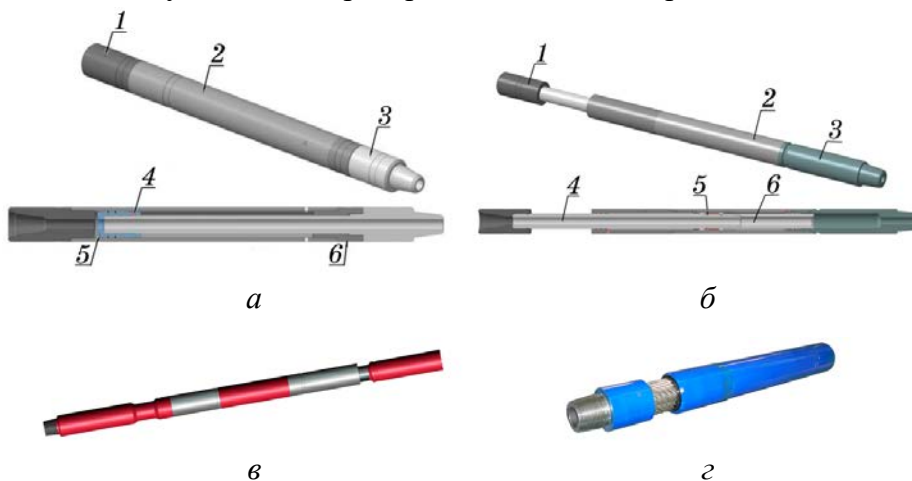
Яс: *а* – механічний (1 – корпус верхній, 2 – корпус, 3 – шток, 4 – шпеник, 5 – хвостовик штока, 6 – корпус нижній); *б* – гідравлічний (1 – перевідник, 2 – корок, 3 – корпус, 4 – шток, 5 – поршень, 6 – хвостовик штока); *в* – hydraulic-fishing-drilling, *г* – крутильний «Shock Turn»
